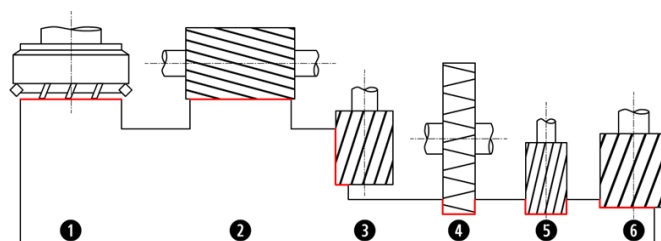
Les diverses opérations d'usinage sur le fraisage [20]
